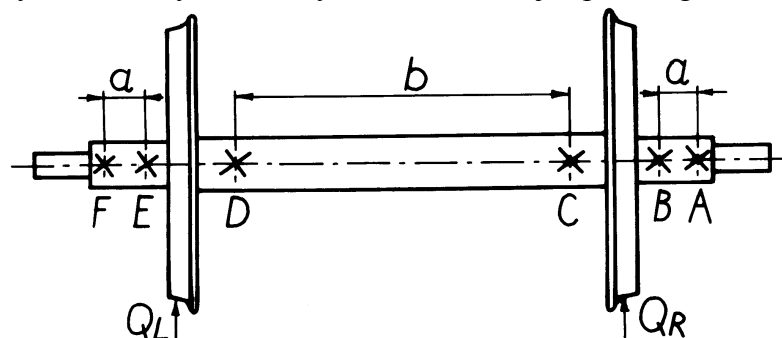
Przekroje pomiarowe momentów zginających osi kolejowego zestawu kołowego.
